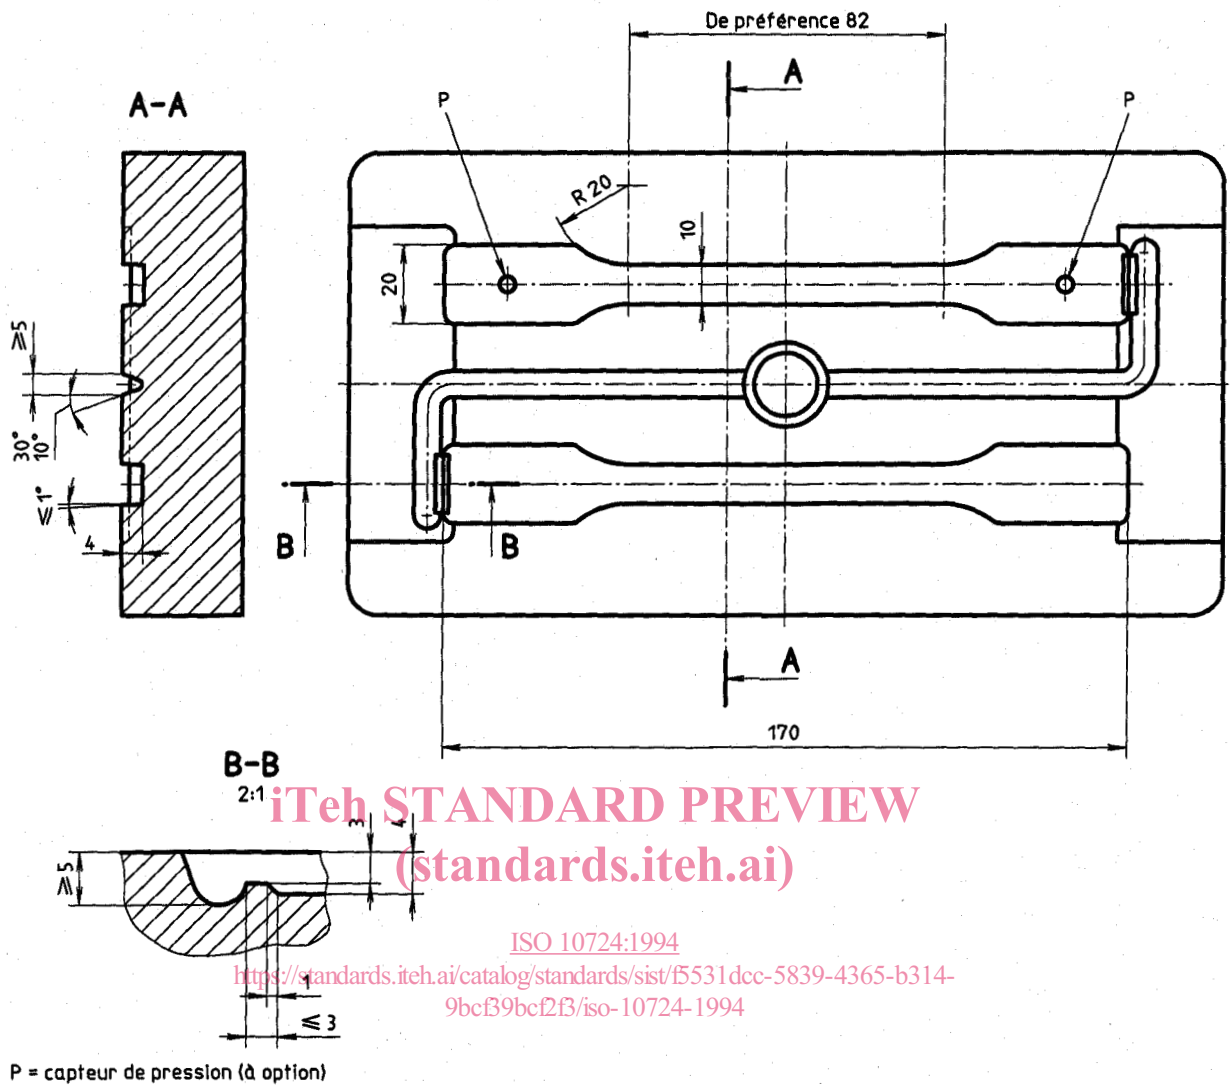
Moule d'injection ISO pour éprouvettes à usages multiples selon ISO 3167, type A (type préférentiel) (voir aussi annexe A)
